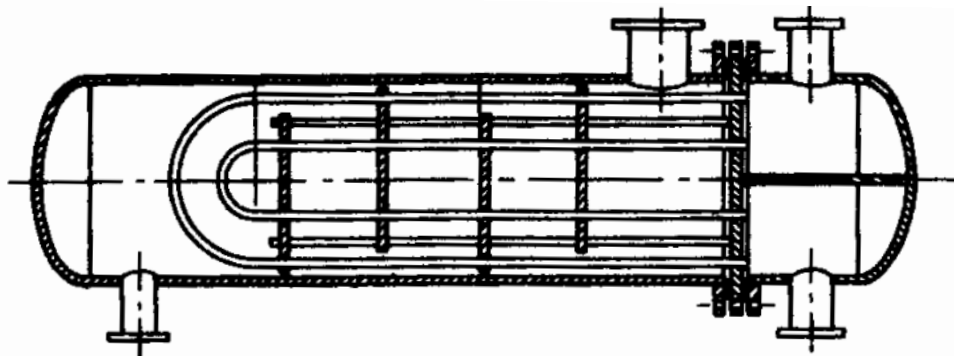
Кожухотрубчатый теплообменник с U-образными трубами
